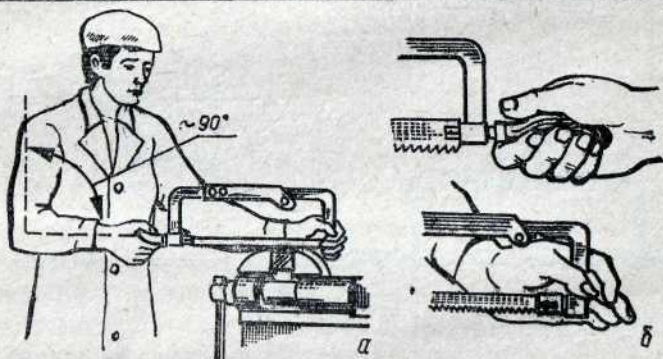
Рабочая поза (а) и хватка инструмента (б) при резании слесарной ножовкой.
